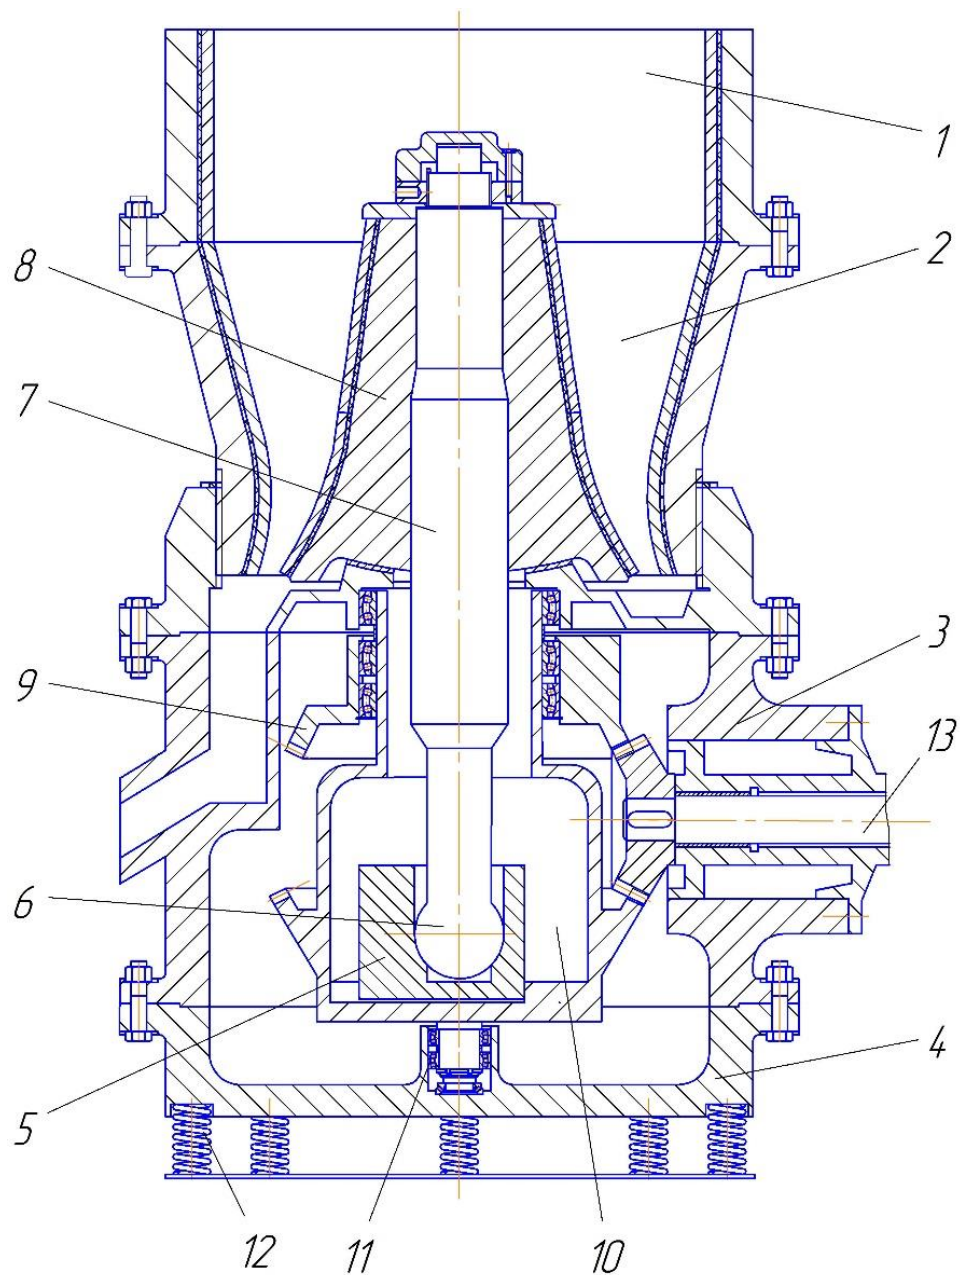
Загальна конструкція інерційної конусної дробарки: 1– завантажувальна секція; 2 – секція, що дробить; 3 – секція приводу; 4 – станина; 5 – вібратор; 6 – шарнір сферичний підп’ятник; 7 – головний вертикальний вал; 8 – конус, що дробить; 9 – колесо зубчасте конічне; 10 – стакан; 11 – вузол підшипниковий; 12 – пружина; 13 – вал горизонтальний приводний; 14 – підп’ятник сферичний.
